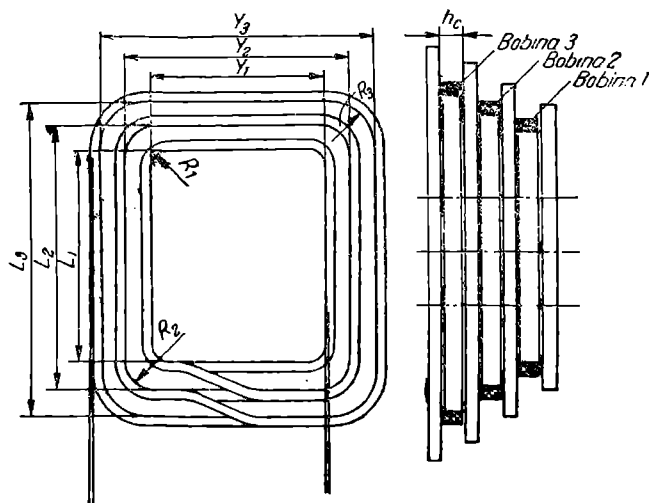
Dimensiunile șablonului pentru confecționarea bobinelor cu conductor rotund, grupă de bobine concentrice, cu capul de bobine în două etaje, bobinaj într-un singur strat.
